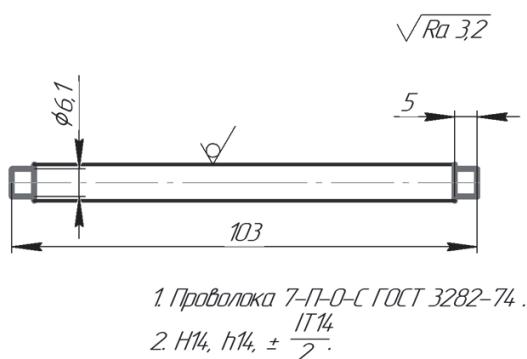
Деталь-представитель для проектирования формообразующего инструмента
